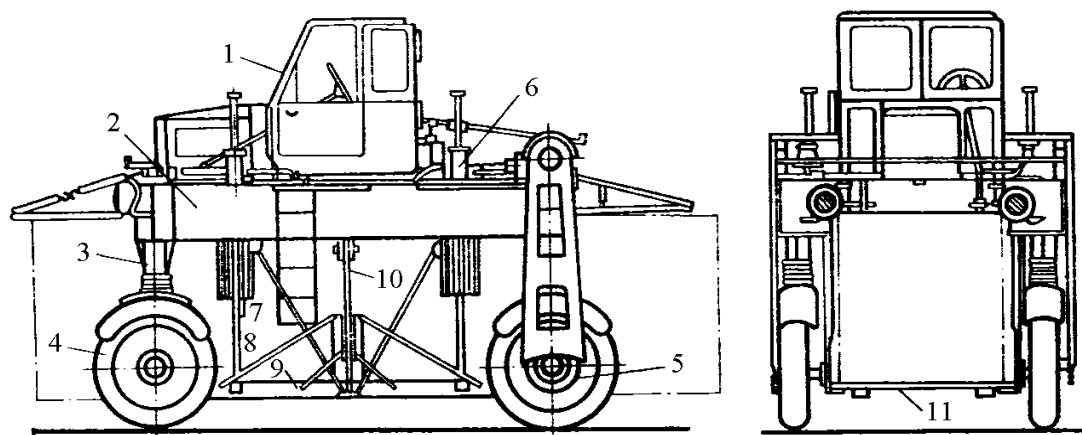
Портальный автолесовоз: 1 – кабина; 2 – рама; 3 – стойка; 4 – колесо; 5 – цепная передача; 6 – цилиндр подъема; 7 – направляющие с кареткой; 8 – грузоподъемная штанга; 9 – грузоподъемная рама; 10 – зажимная штанга; 11 – подставка для пакета
